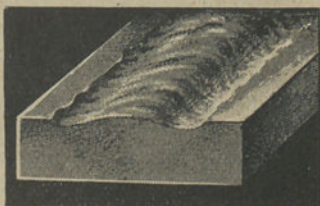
« Canais » nos bordos das soldaduras.
